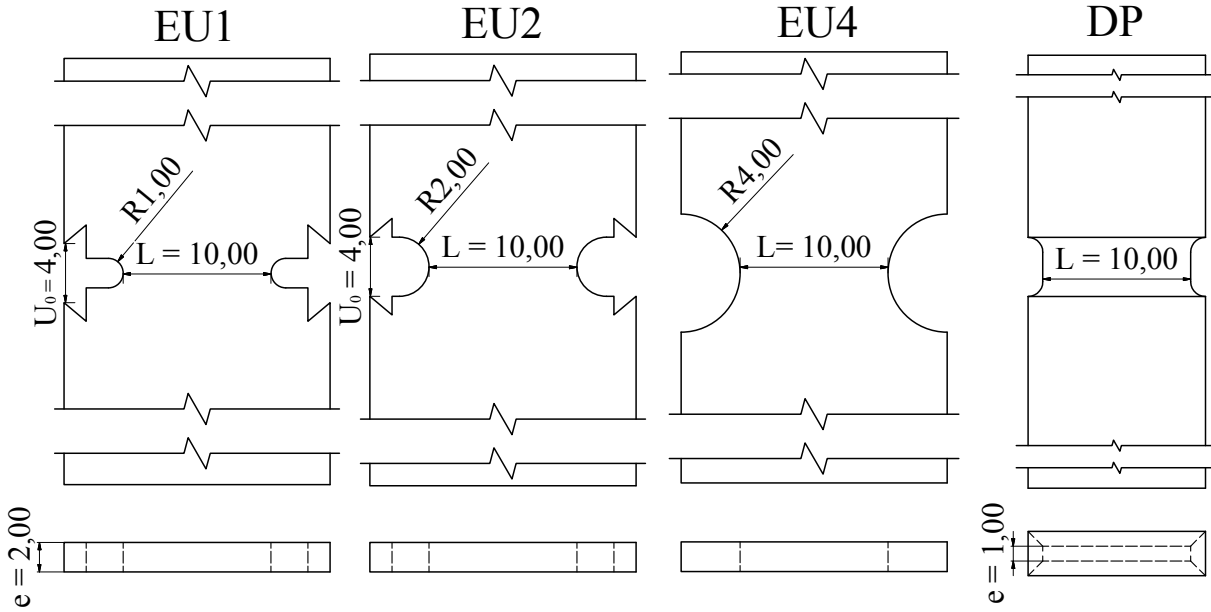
Géométries des éprouvettes EU et de l'éprouvette DP - dimensions en millimètres
